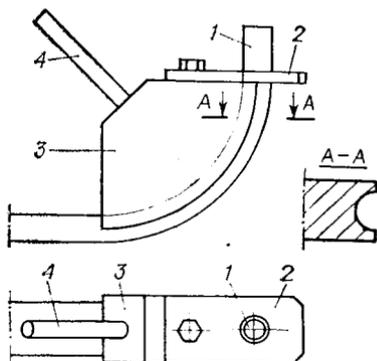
Приспособление для гнутья труб малого диаметра:
